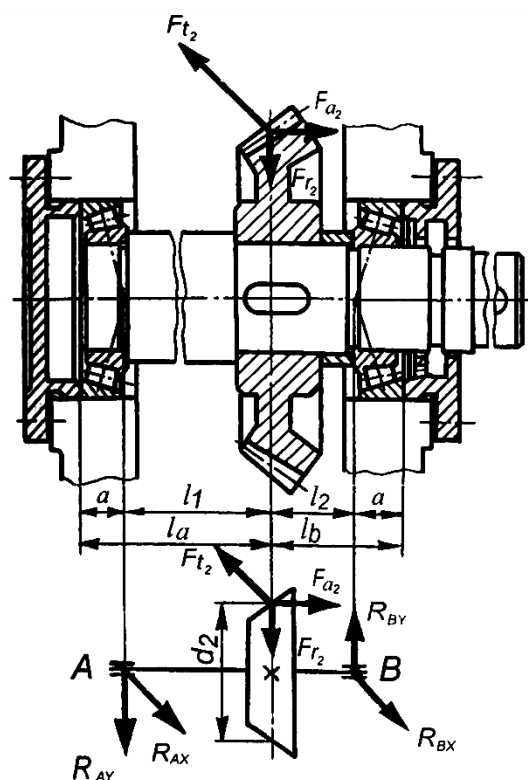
Подшипниковые узлы ведомого вала конического редуктора
